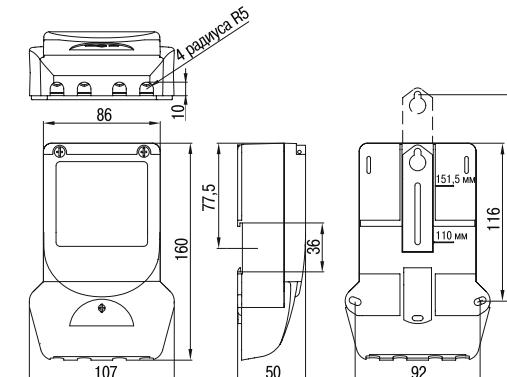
Габаритные и присоединительные размеры счётчиков габарита корпуса 3
